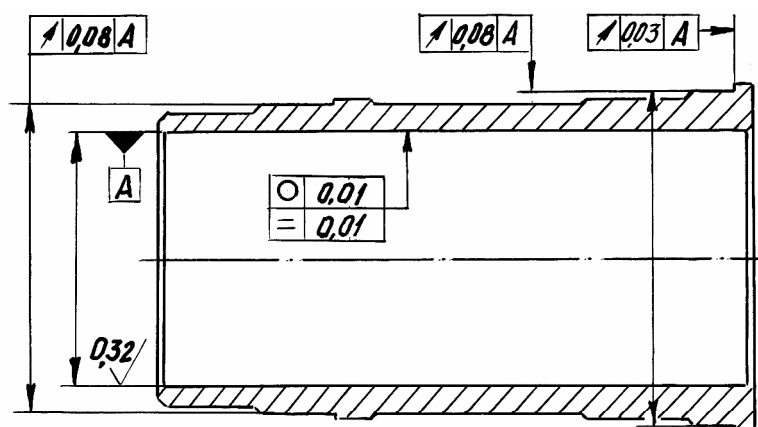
Гильза цилиндра (размерными линиями указаны контролируемые размеры)
